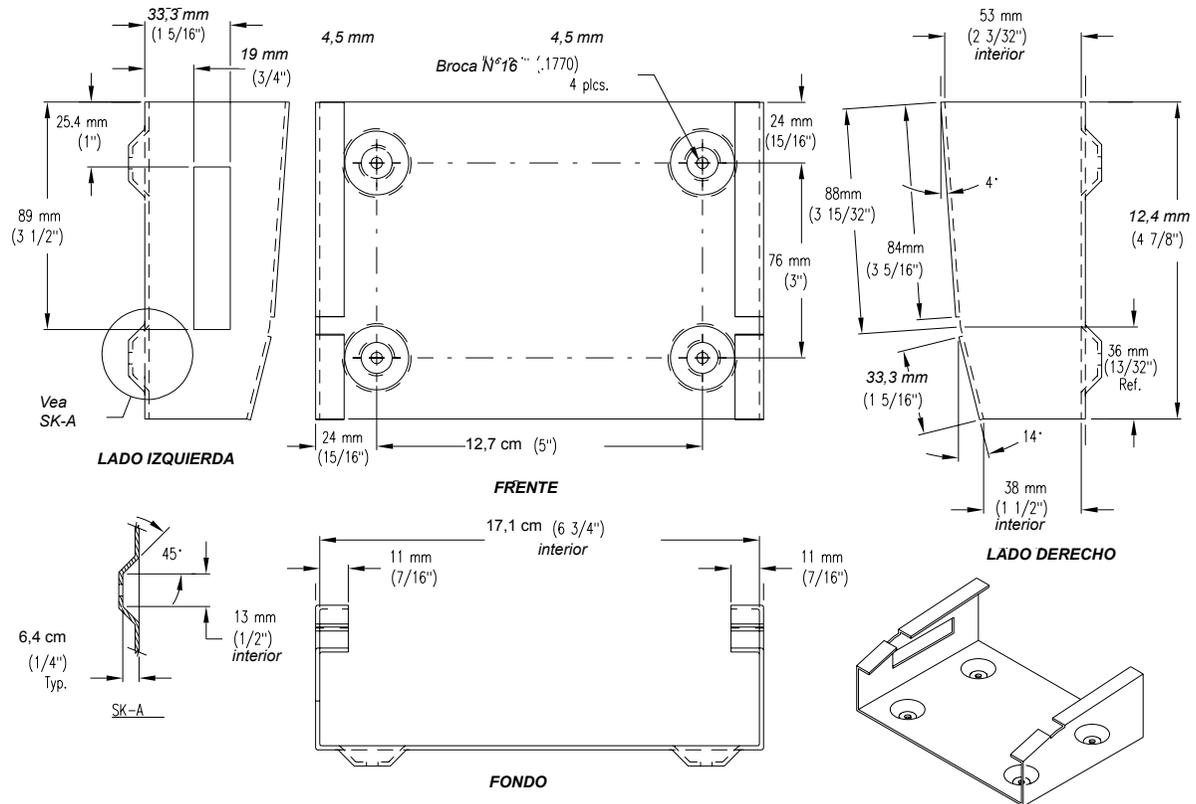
Dimensiones del Montaje del Soporte de la Impresora
